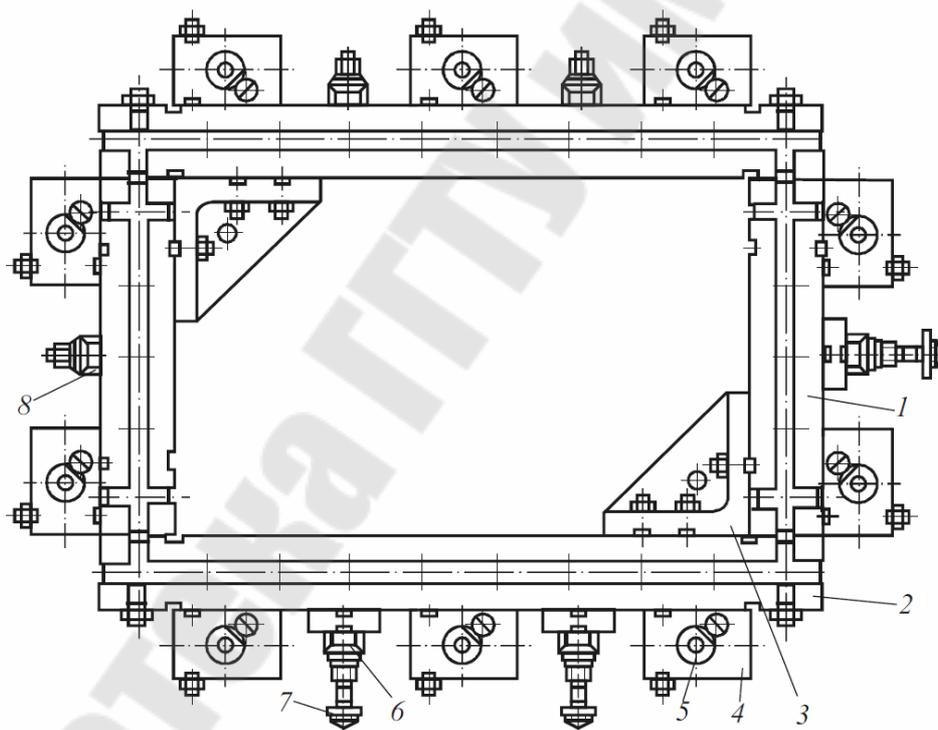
Универсально-сборный прямоугольный накладной кондуктор для сверления десяти отверстий [4]
